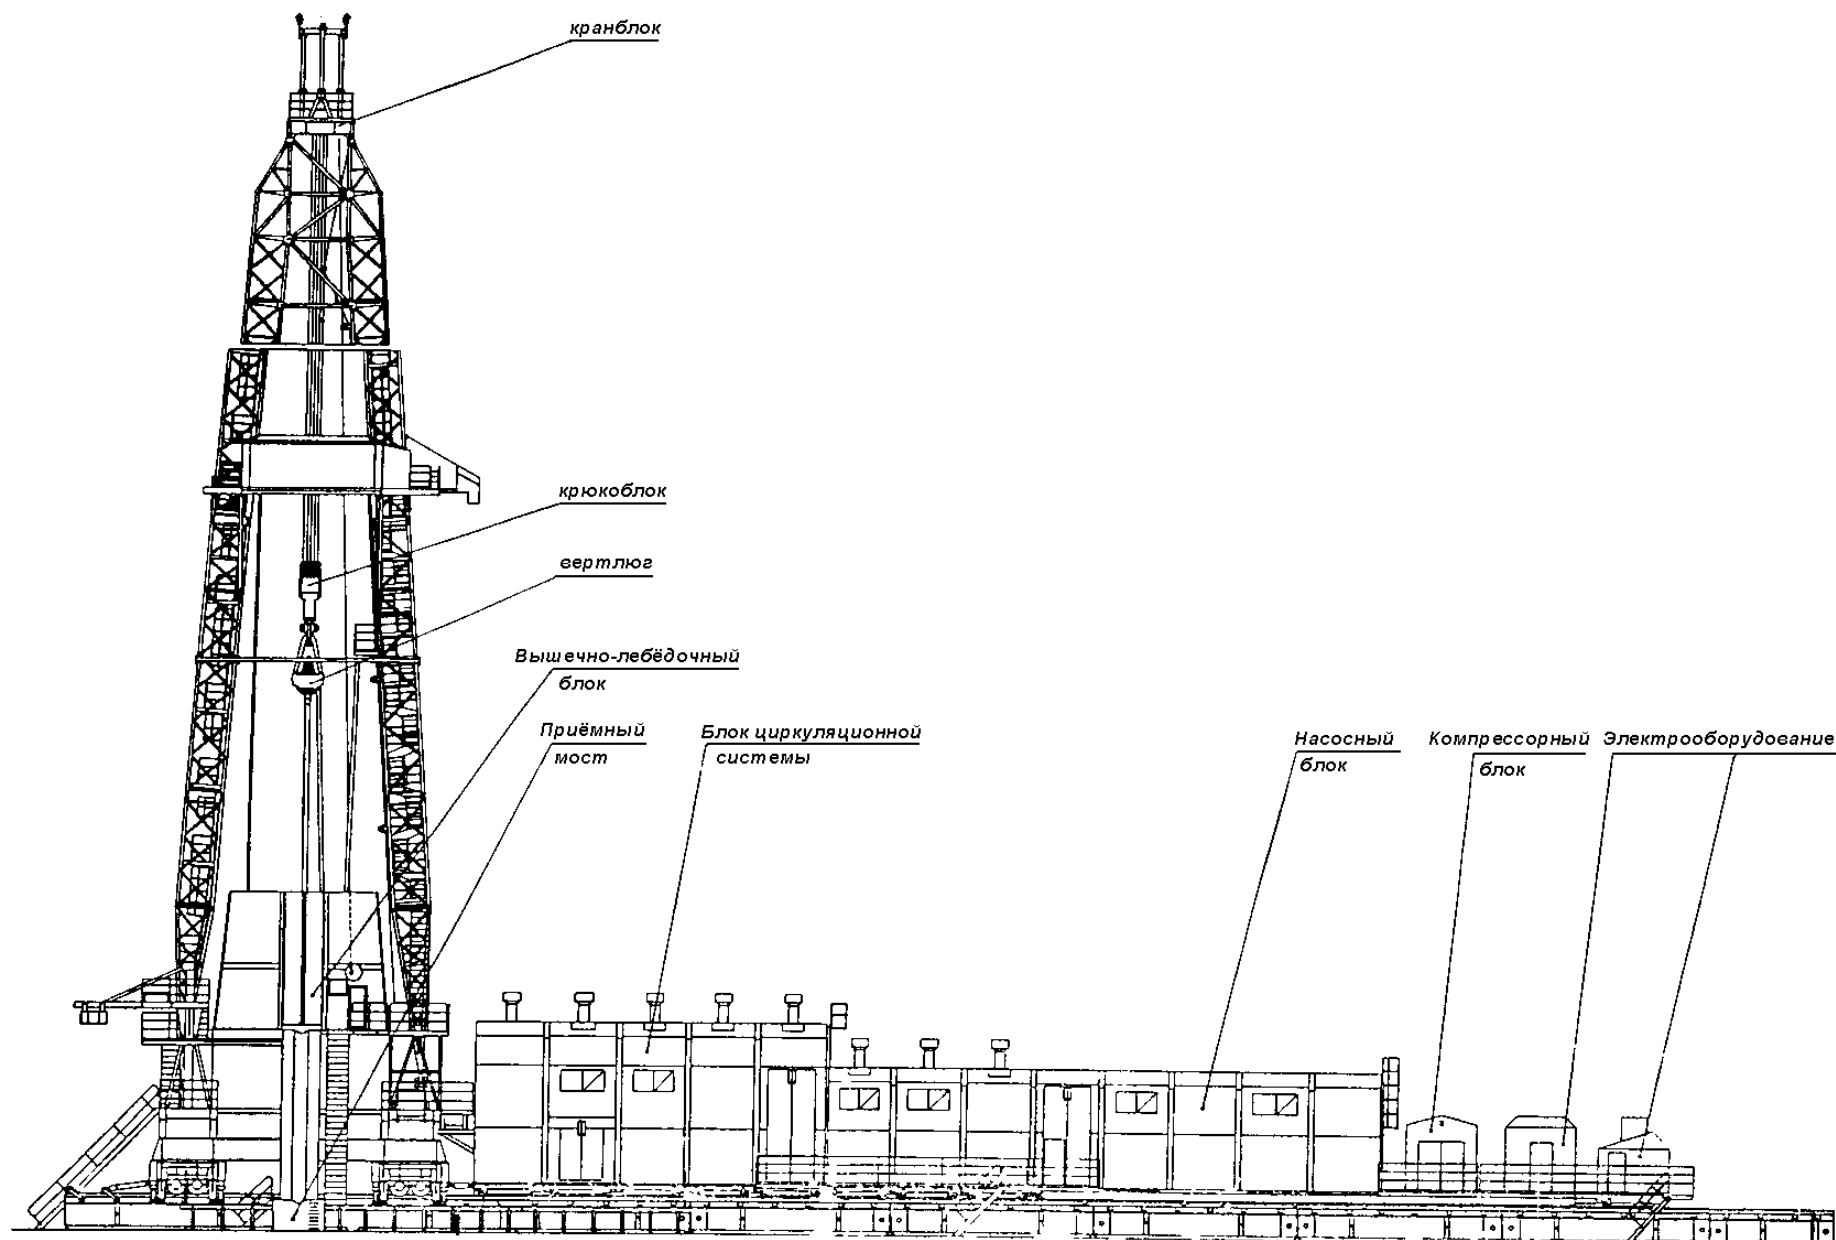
Общий вид буровой установки (вид сбоку)
